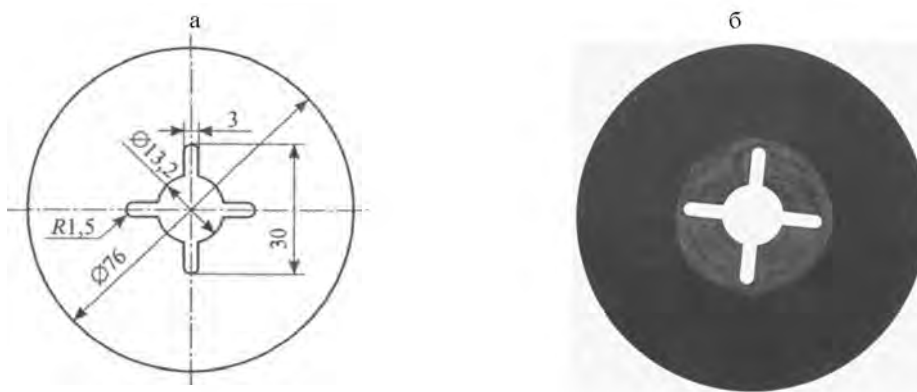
а – конструктивное исполнение заготовки распиловочного диска; б – фотография распиловочного диска после выполнения операции шаржирования его боковых поверхностей
